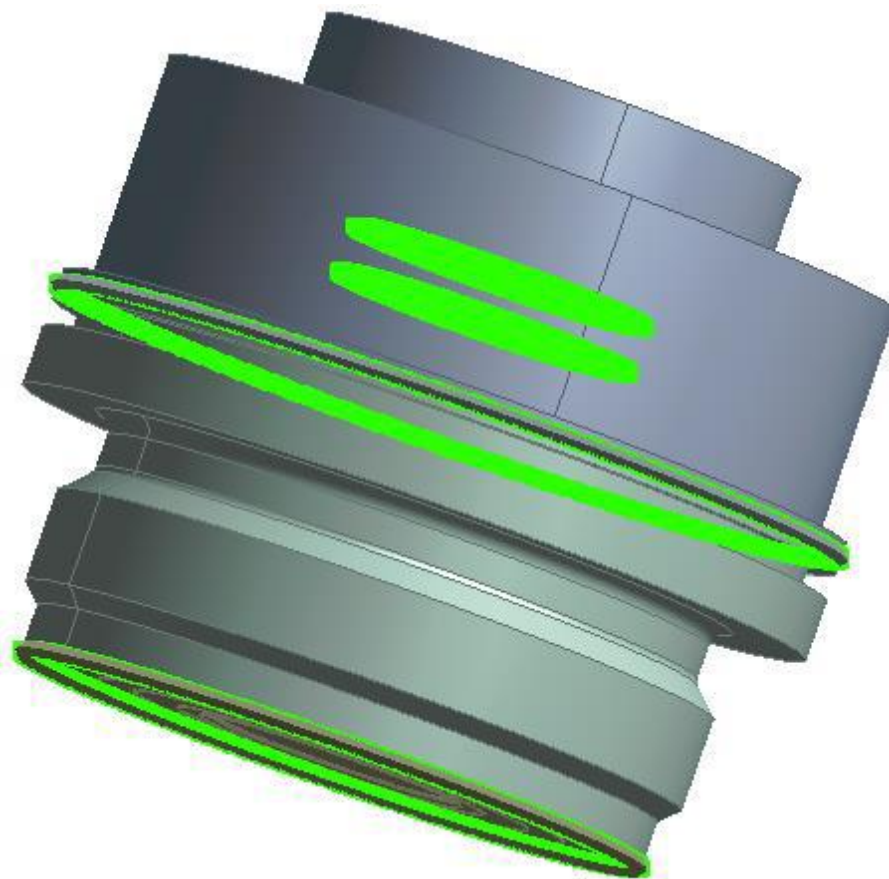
Сварные соединения на модели датчика
